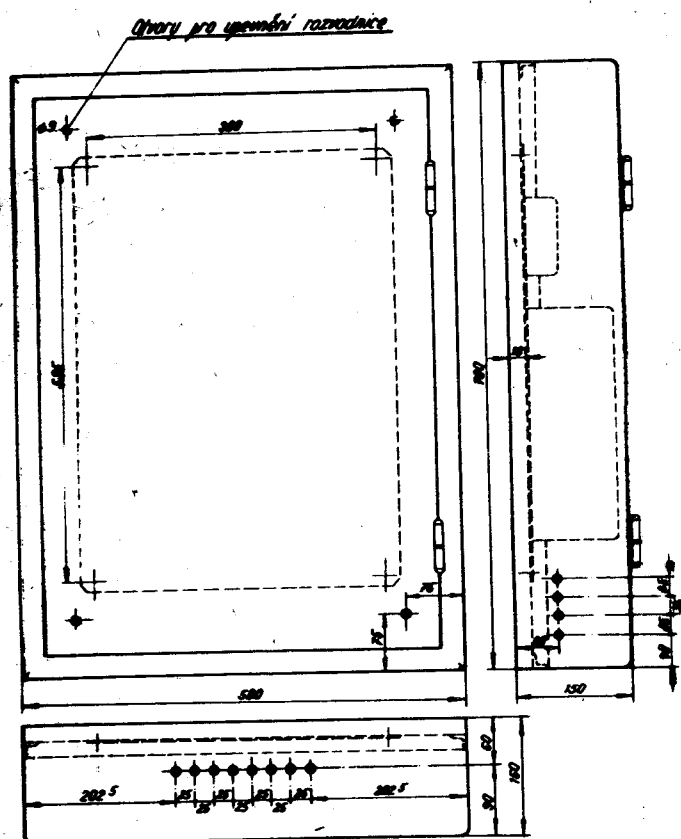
Základní deska se zesilovací soupravou TAZ 02 a montážními rozměry
